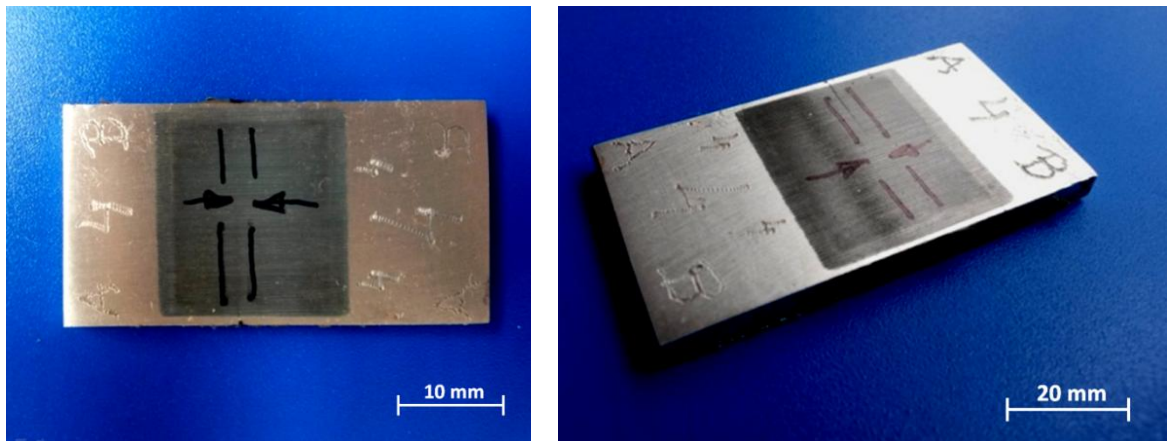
Probetas cortadas para proceder a la apertura de la fisura
